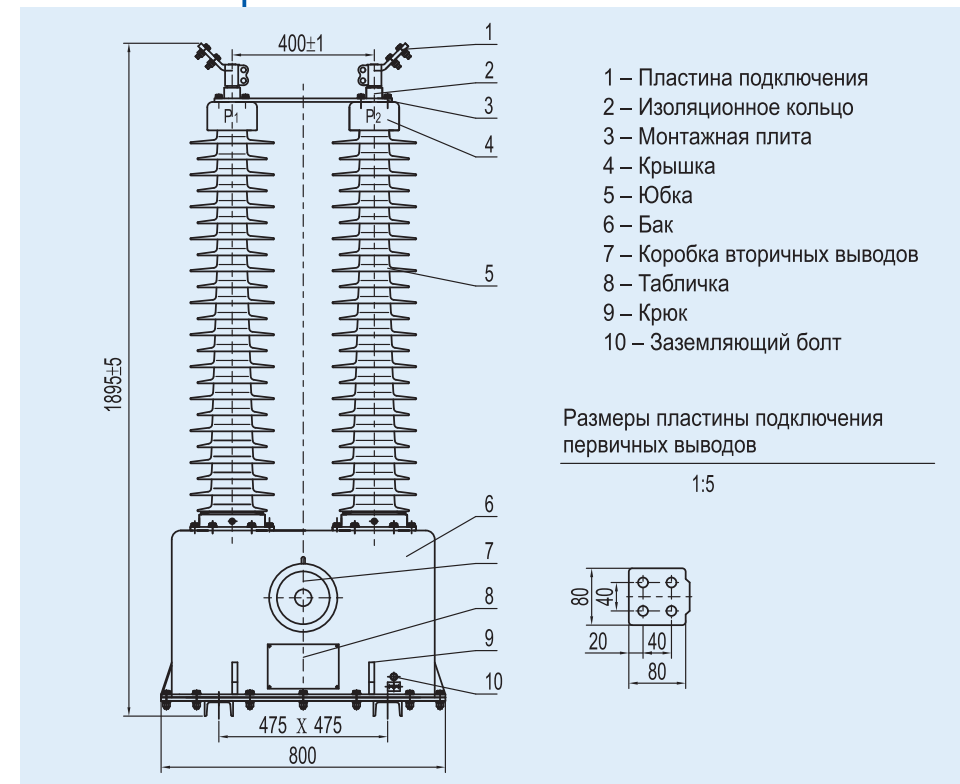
Внешний вид и размеры трансформатора тока LGB-110W2
